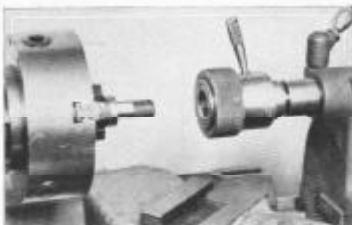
Terraja montada en la contrapunta para filetear piezas cortas
